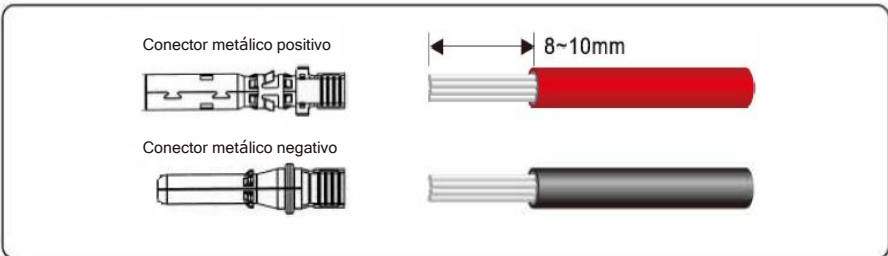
Pelado de la capa de aislamiento de un cable de CC (unidad: mm)
